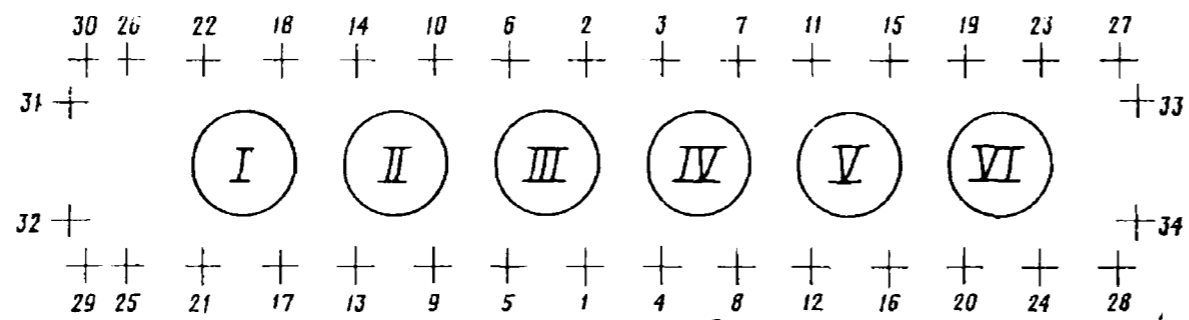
Последовательность затяжки до упора гаек крепления крышки головки блока
